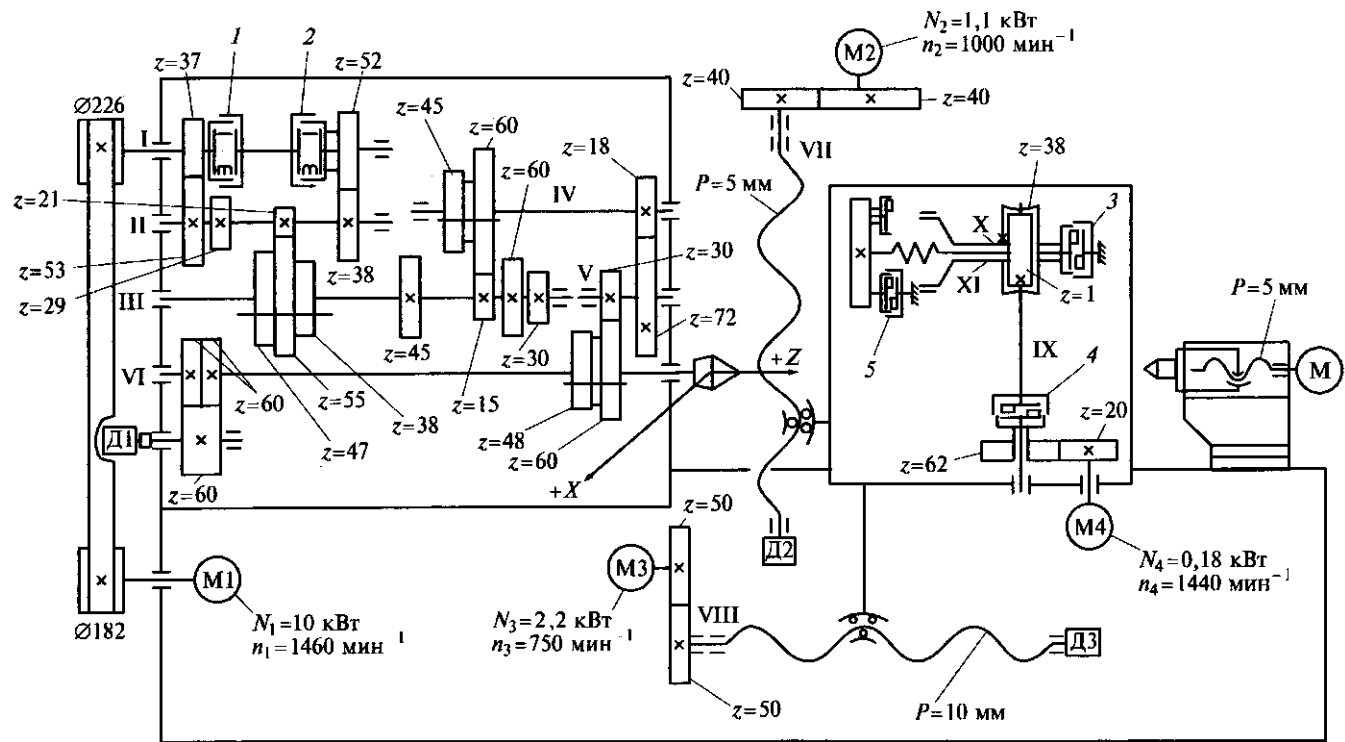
Кинематическая схема токарного патронно-центрового станка с с оперативной системой ЧПУ:
